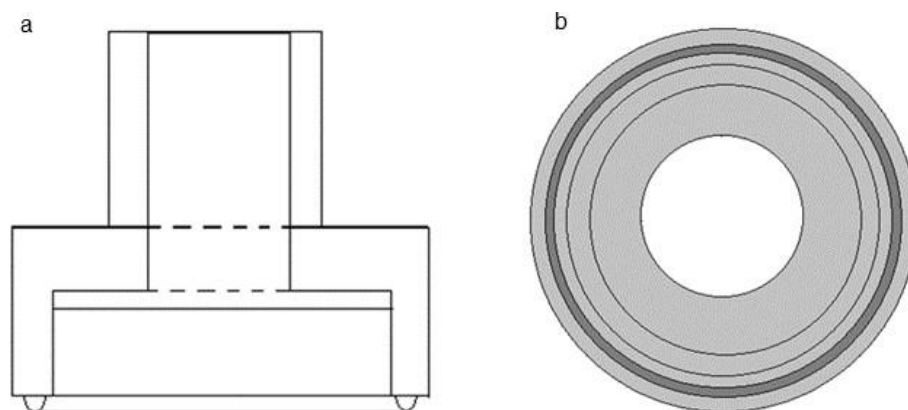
sezione laterale della bocchetta (a); sezione basale (b).
